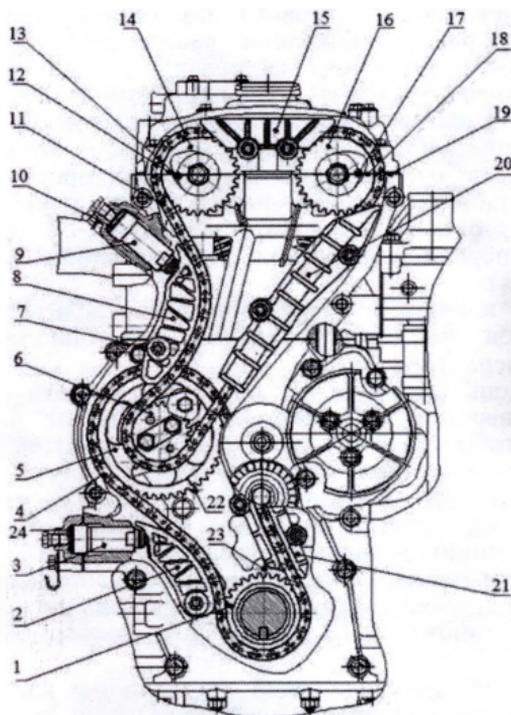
Привод ГРМ с зубчатыми цепями
